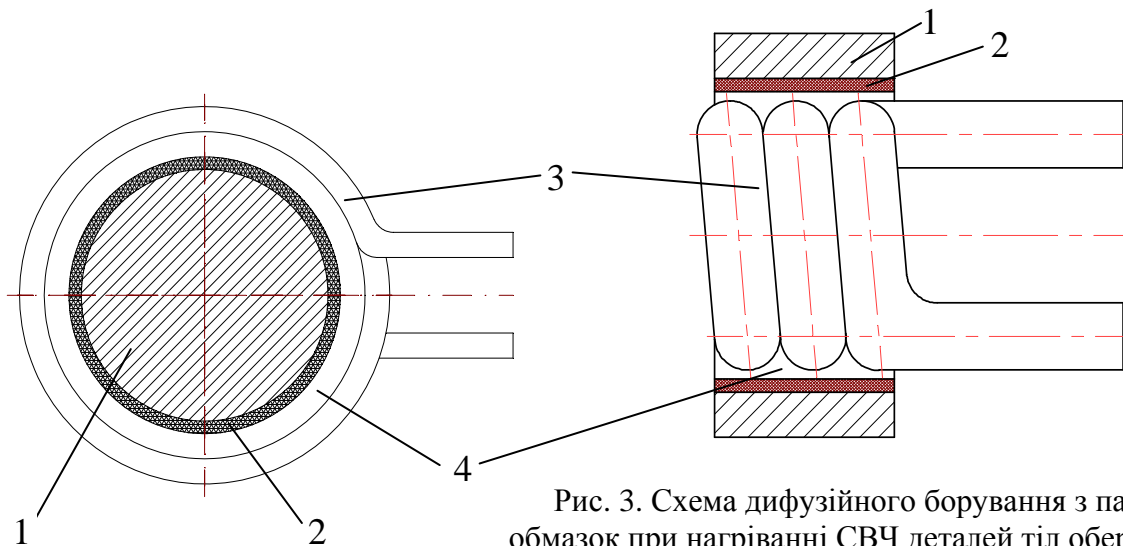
Схема дифузійного борування з паст і обмазок при нагріванні СВЧ деталей тіл обертання: 1 – зміцнювальна деталь; 2 – обмазка; 3 – індуктор; 4 – зазор між деталлю та індуктором
